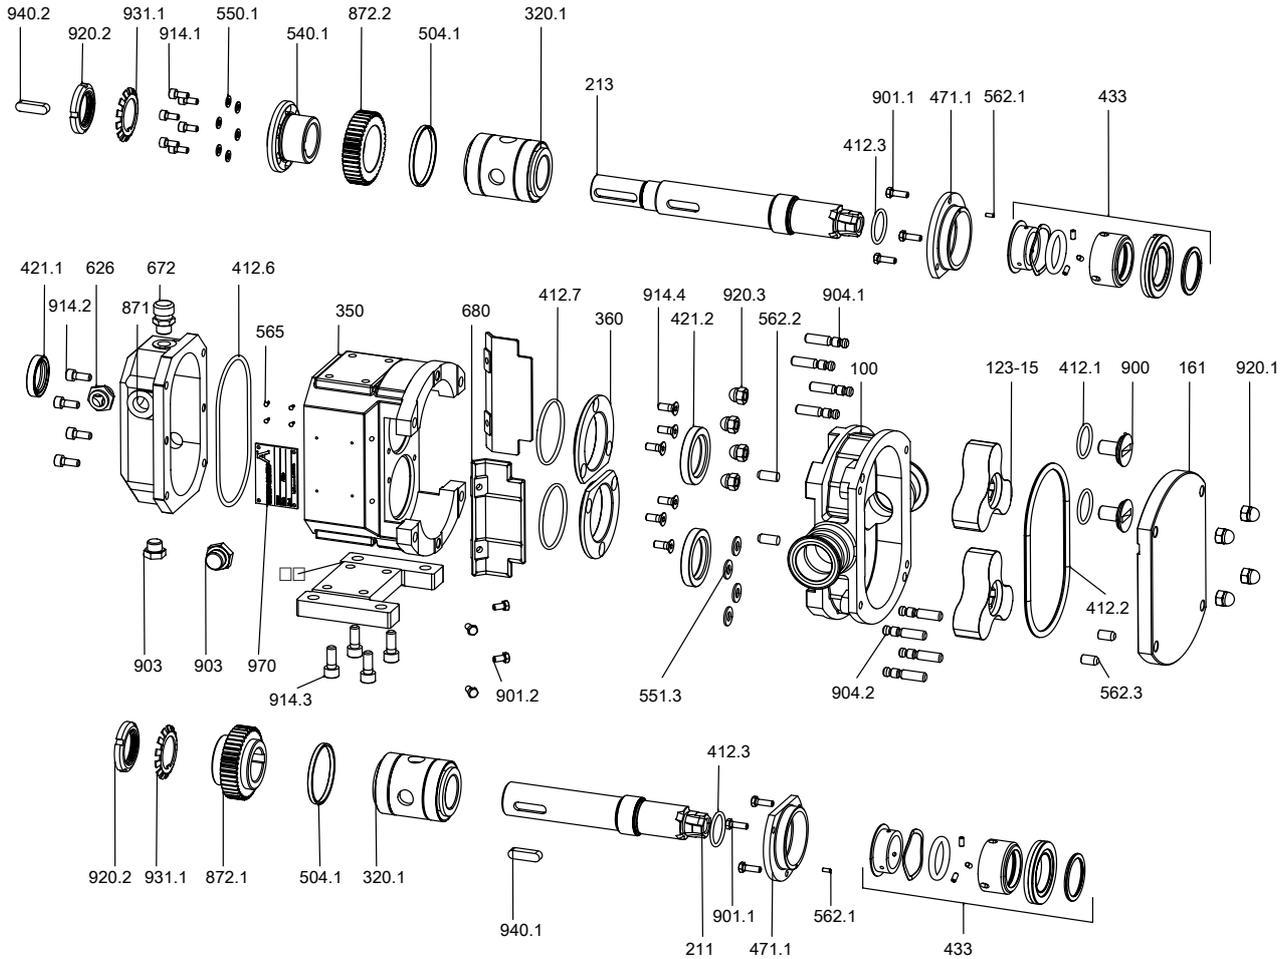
Explosionszeichnung Vitalobe Baugröße 105, 110, 115
